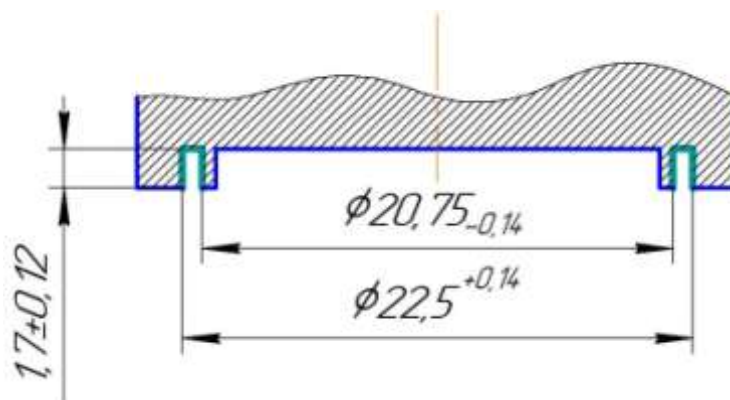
Эскиз обрабатываемой поверхности паза
